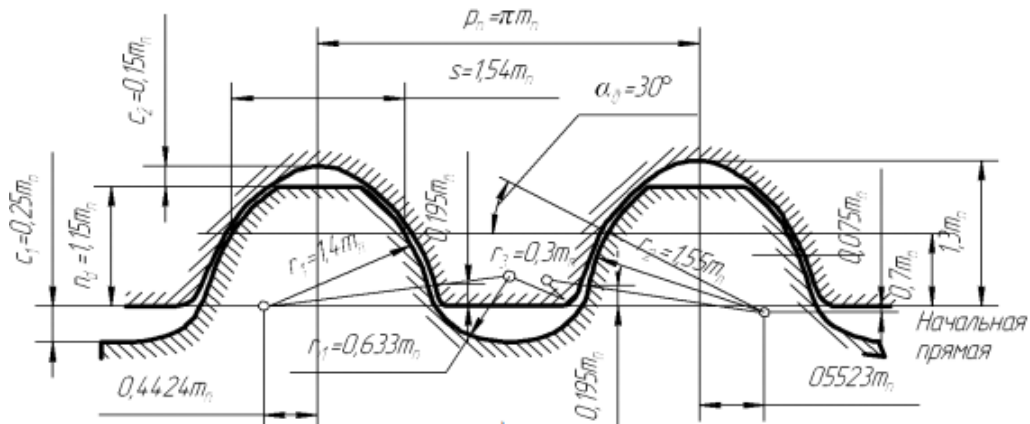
Исходный контур зубьев шестерни и колеса для передачи Новикова с одной линией зацепления.
